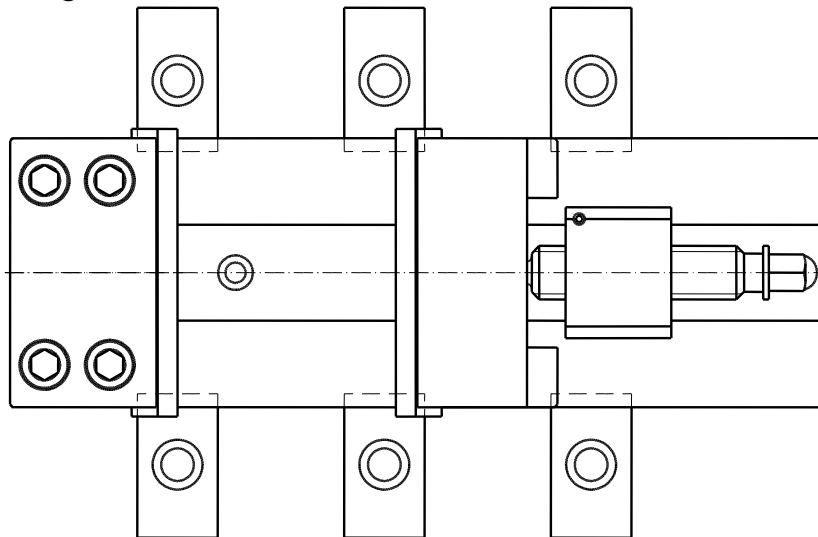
Befestigung des Schraubstocks Typ 6620 auf dem WM-Tisch.
